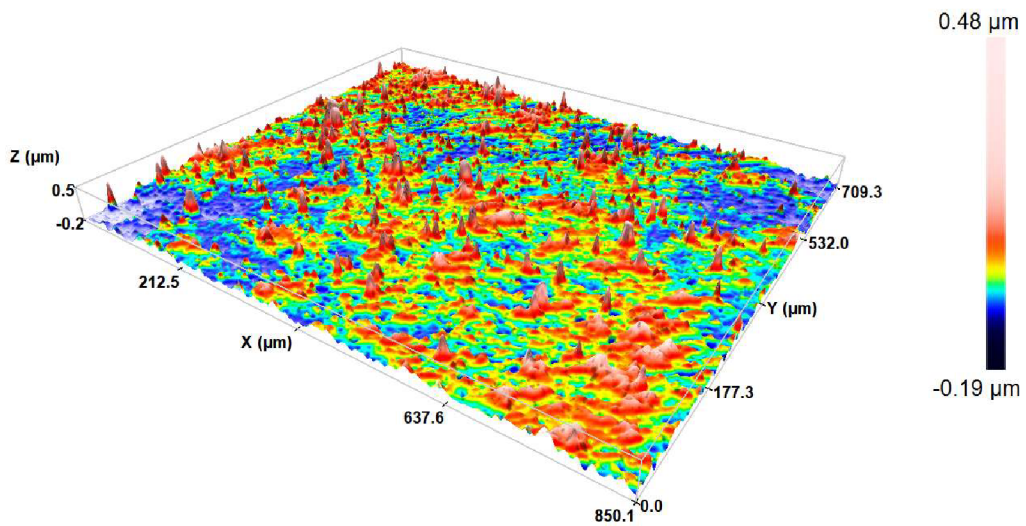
Geometrický profil povrchu – substrát ČSN 19 830
